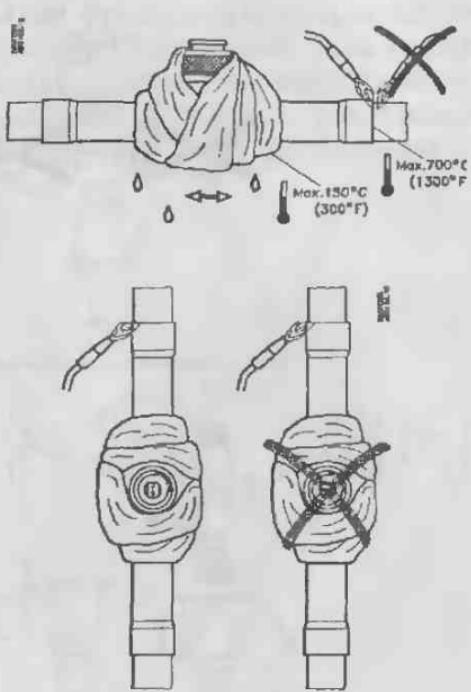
Фрагмент инструкции «Danfoss» по монтажу шарового вентиля GBC
